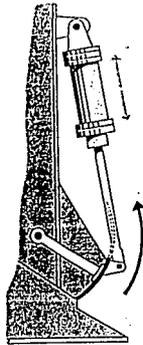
APERTURA Y CIERRE DE COMPUERTAS EN SILOS PARA UNA PLANTA DE PRODUCCION DE HORMIGON.
